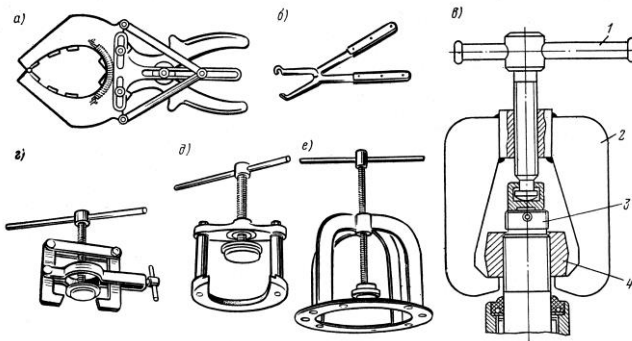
Пристрої для розбирання агрегатів і механізмів АТЗ:
